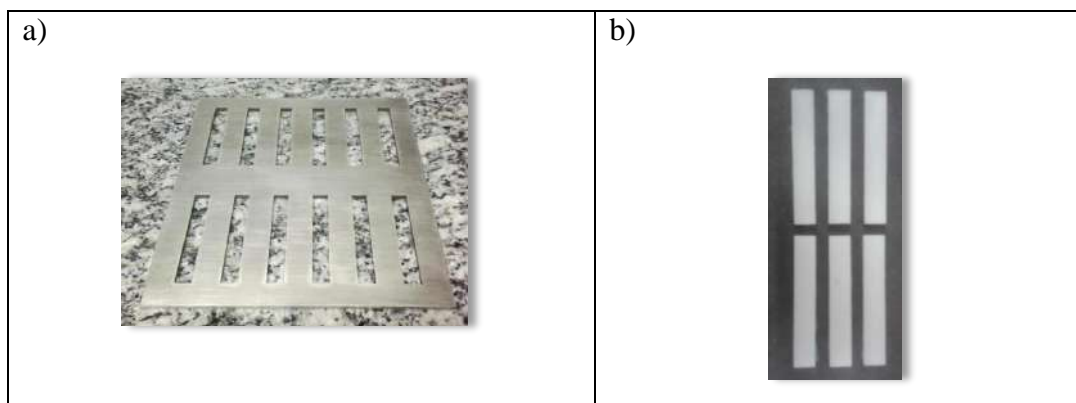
Molde para confecção de corpos de prova de DMTA utilizando moldagem por compressão (a), e corpos de prova após o acabamento final (b).
